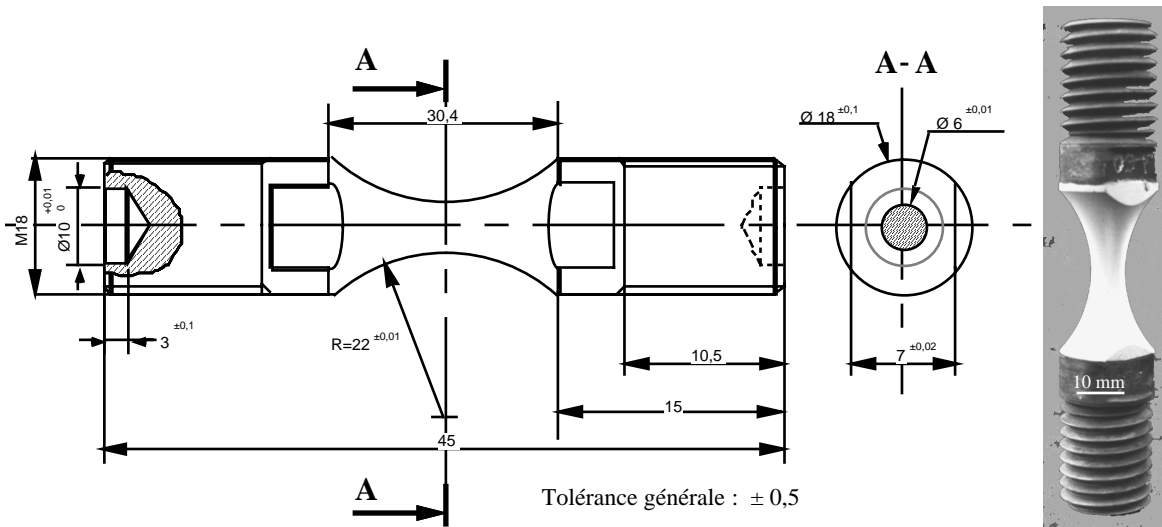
dessin de définition de l'éprouvette AG2C et photographie après dépôt de la barrière thermique.
